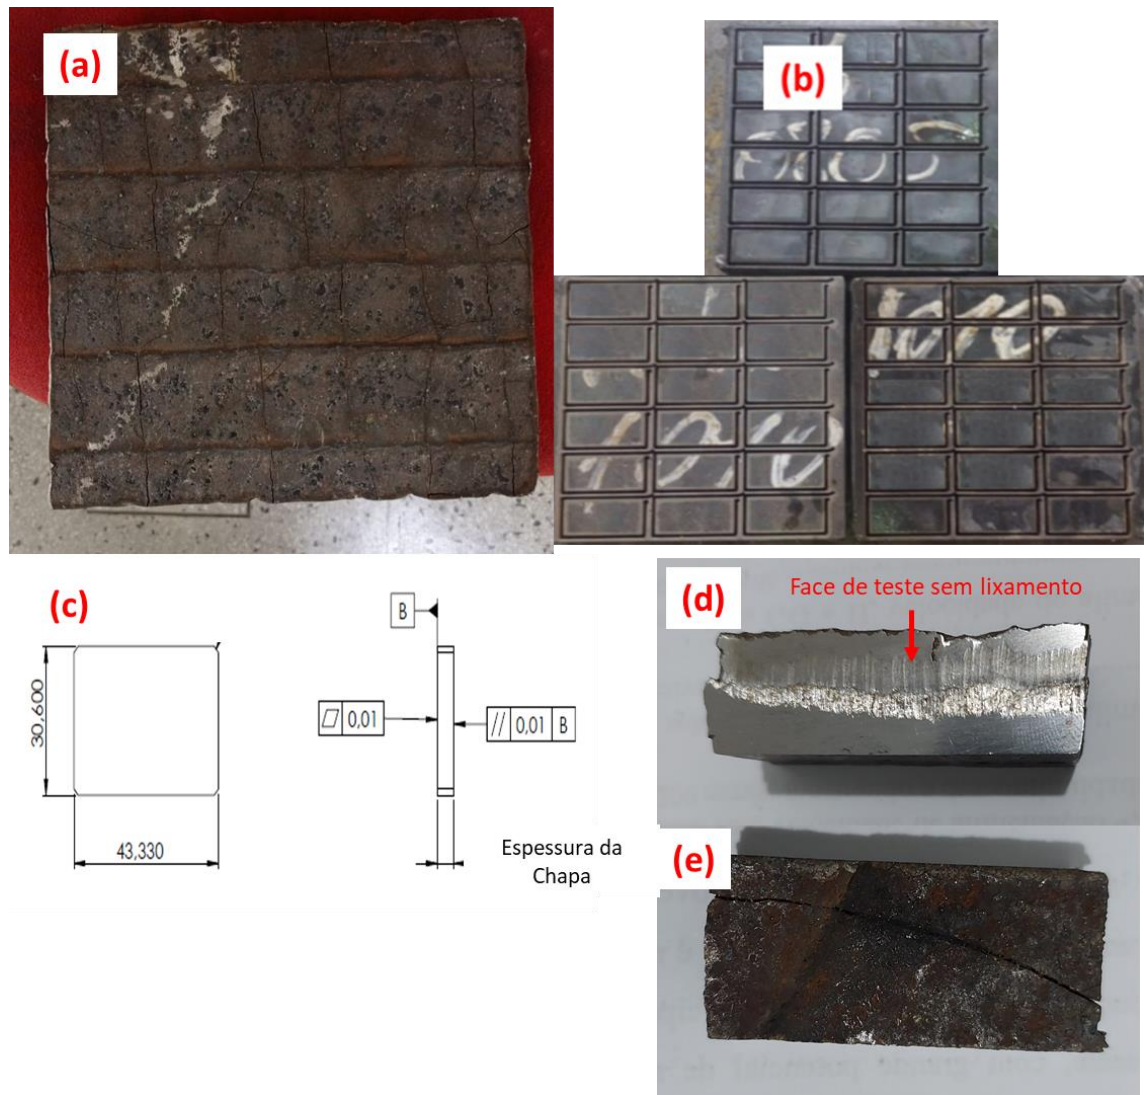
Preparo dos corpos de prova. (a) Amostra de chapa soldada; (b) Chapas após corte por jato d’água; (c) Desenho técnico; (d) Corpo de prova retirada da chapa amostra, face de testes voltada para cima; (e) Corpo de prova retirada da chapa de amostra.
